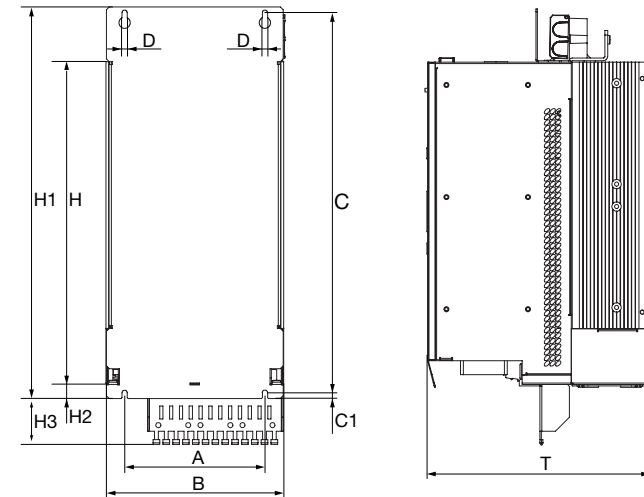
Maßzeichnung Gehäusevariante Wandmontage BG5 + BG6A (Darstellung symbolisch)
